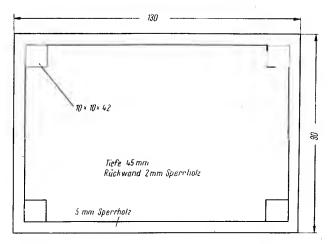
Maßskizze für das Holzgehäuse des Durchgangsprüfers
